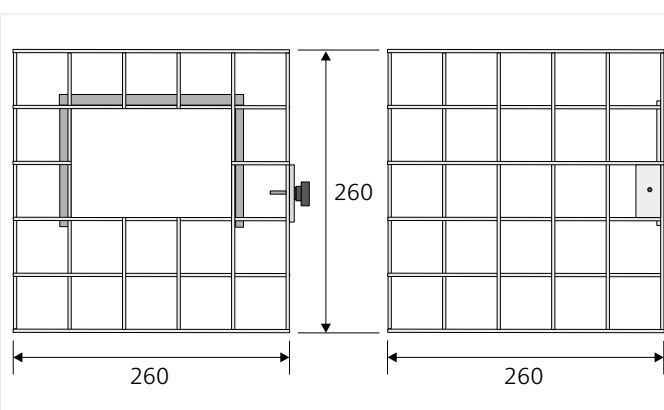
Schutzkorb GDP Front- und Seitenansicht
